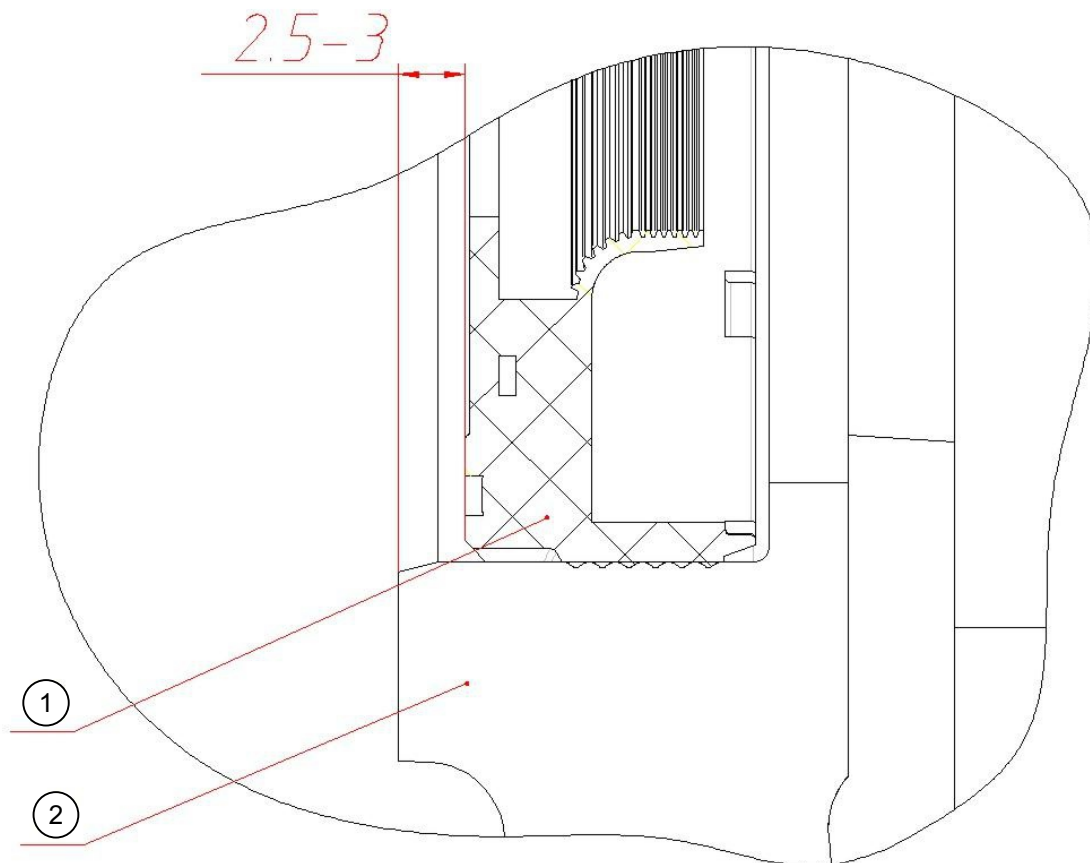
Зазор: торец манжеты - торец передней крышки
